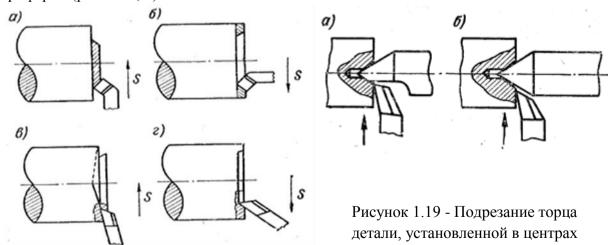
Обработка торца детали закрепленной в патроне
